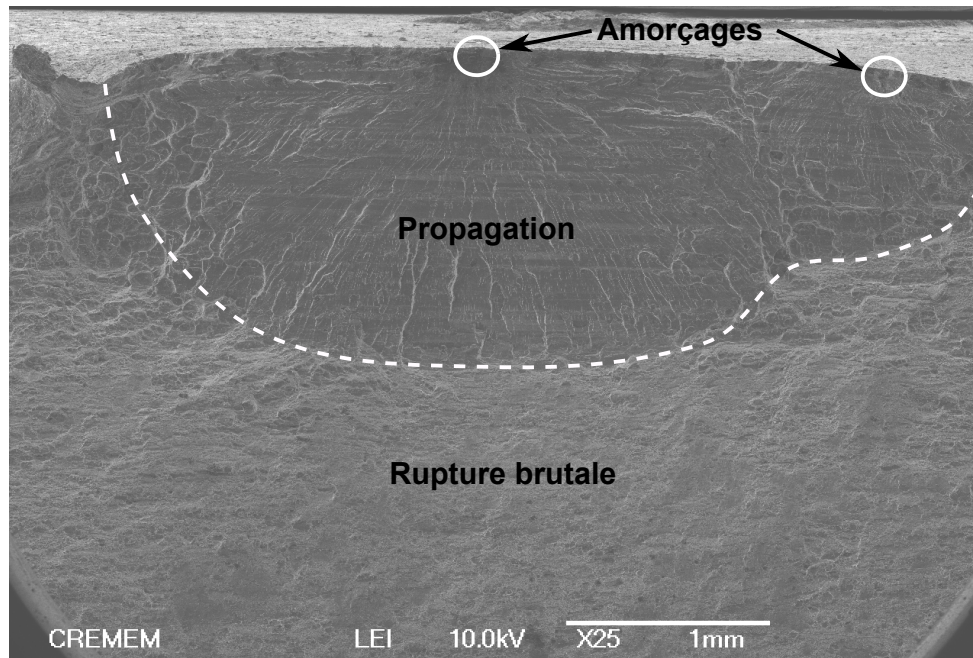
Allure typique des faciès de rupture en fatigue des joints soudés par FSW
